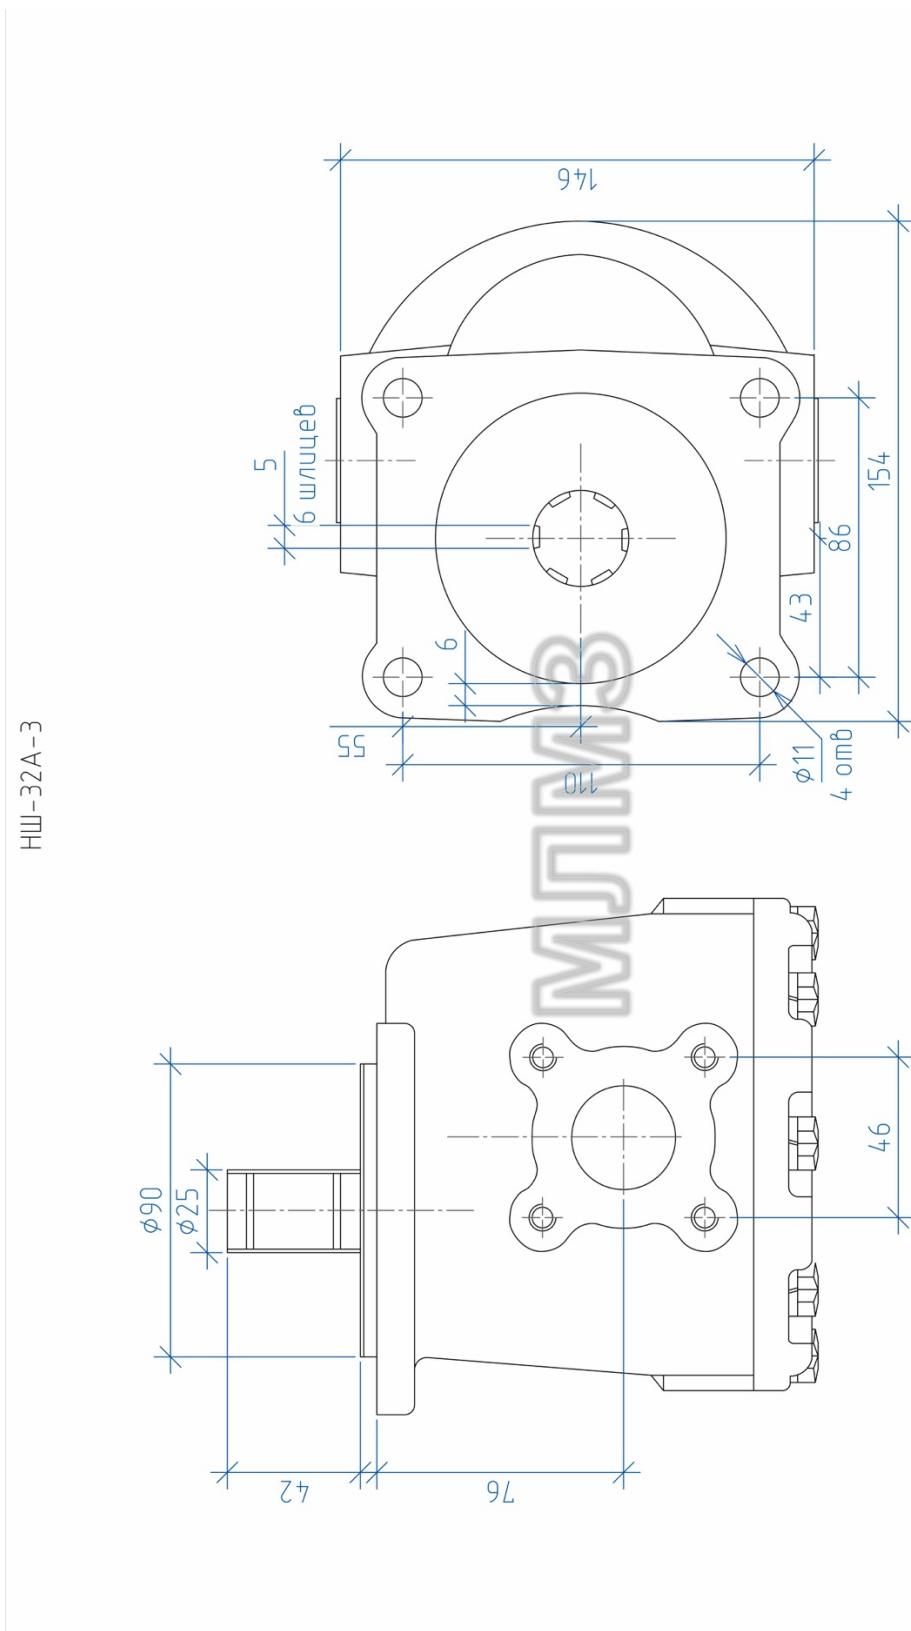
Насосы шестеренные НШ32А-3, НШ32А-3Л. Габаритные и присоединительные размеры.
